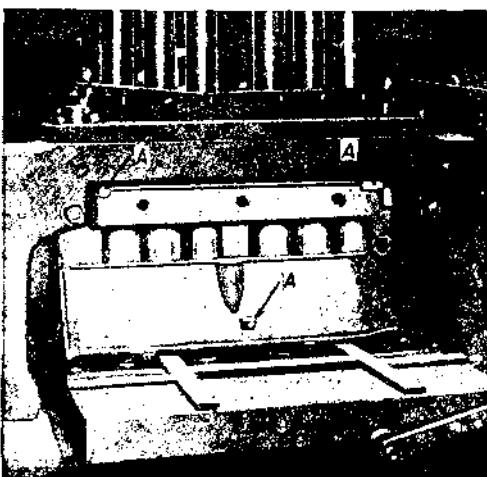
Опорные площадки для установки блока при фрезеровке.
